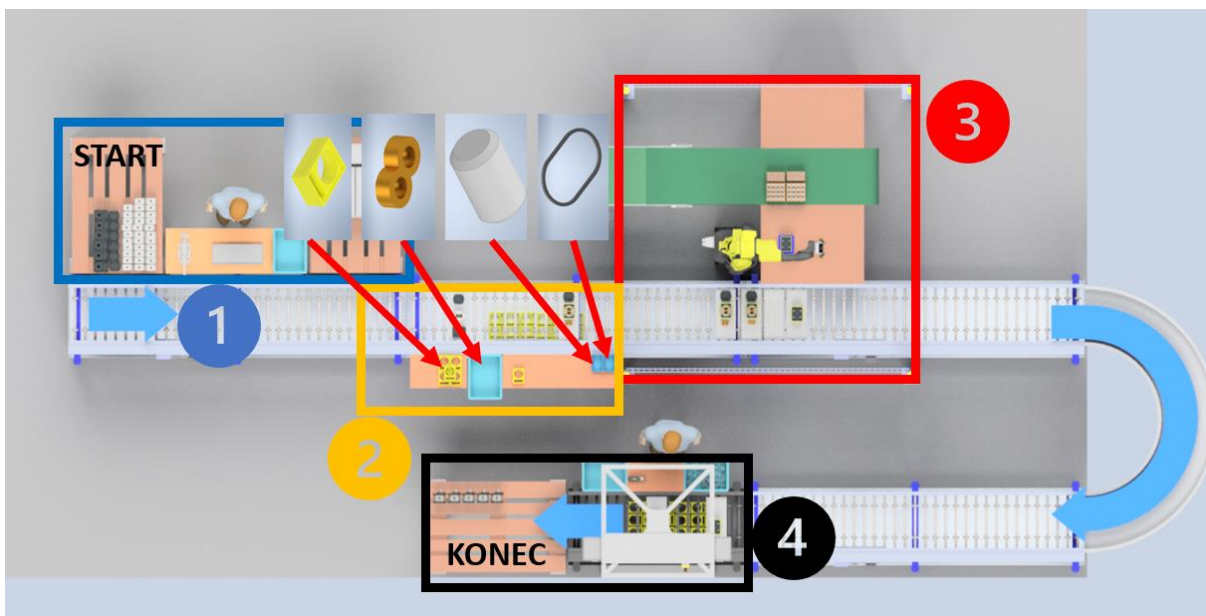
Varianta č. 1: Rozložení stanovišť
